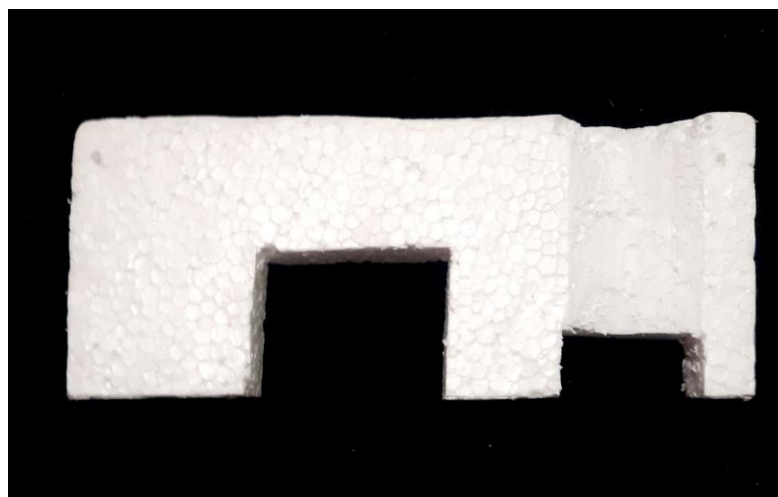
Visão da parte frontal da caixa com a parte “raspada” para o cano
